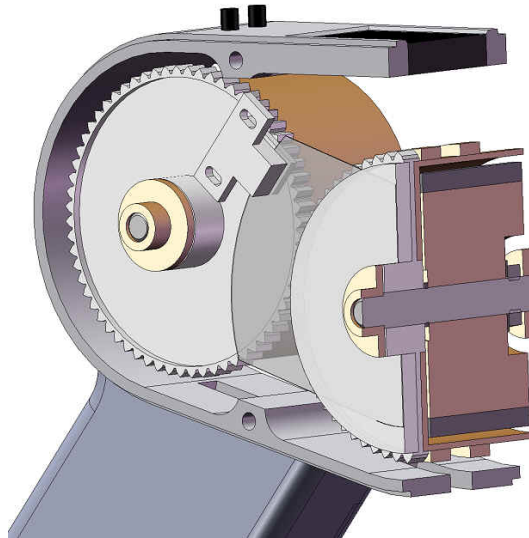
Mecanismo de transmissão interna e elemento de medição
